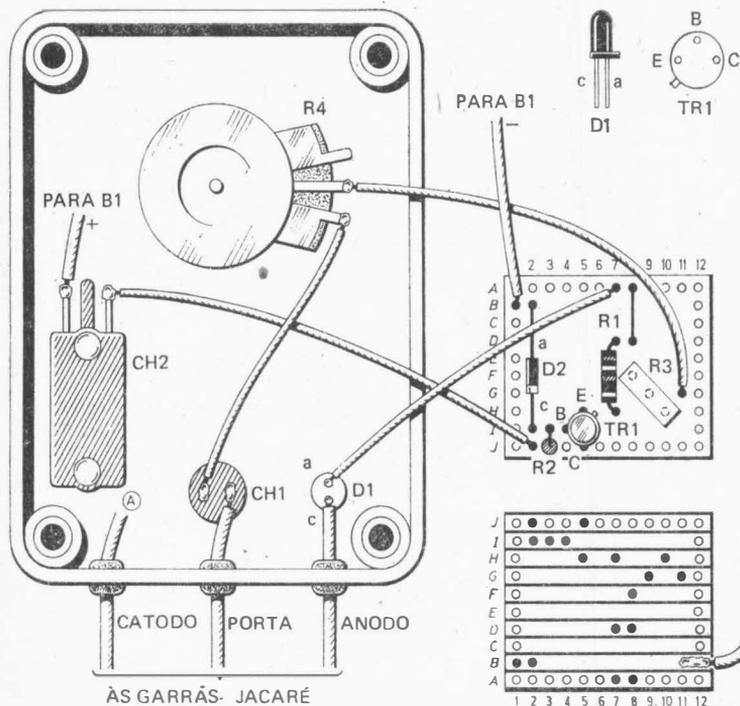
Detalhes para a montagem do circuito sobre a plaqueta de circuito impresso universal, e ligações entre esta e os demais componentes externos. No protótipo a plaqueta não foi fixada à caixa, ficando suspensa apenas pela fiação. Se desejado, uma das bordas da plaqueta poderá ser colada na lateral da caixa. Ao se encaixar R3 devemos entortar convenientemente seus terminais, para que o "trim-pot" fique na posição representada. É de todo recomendável a utilização de fios de cores diferentes para as pontas de prova.
